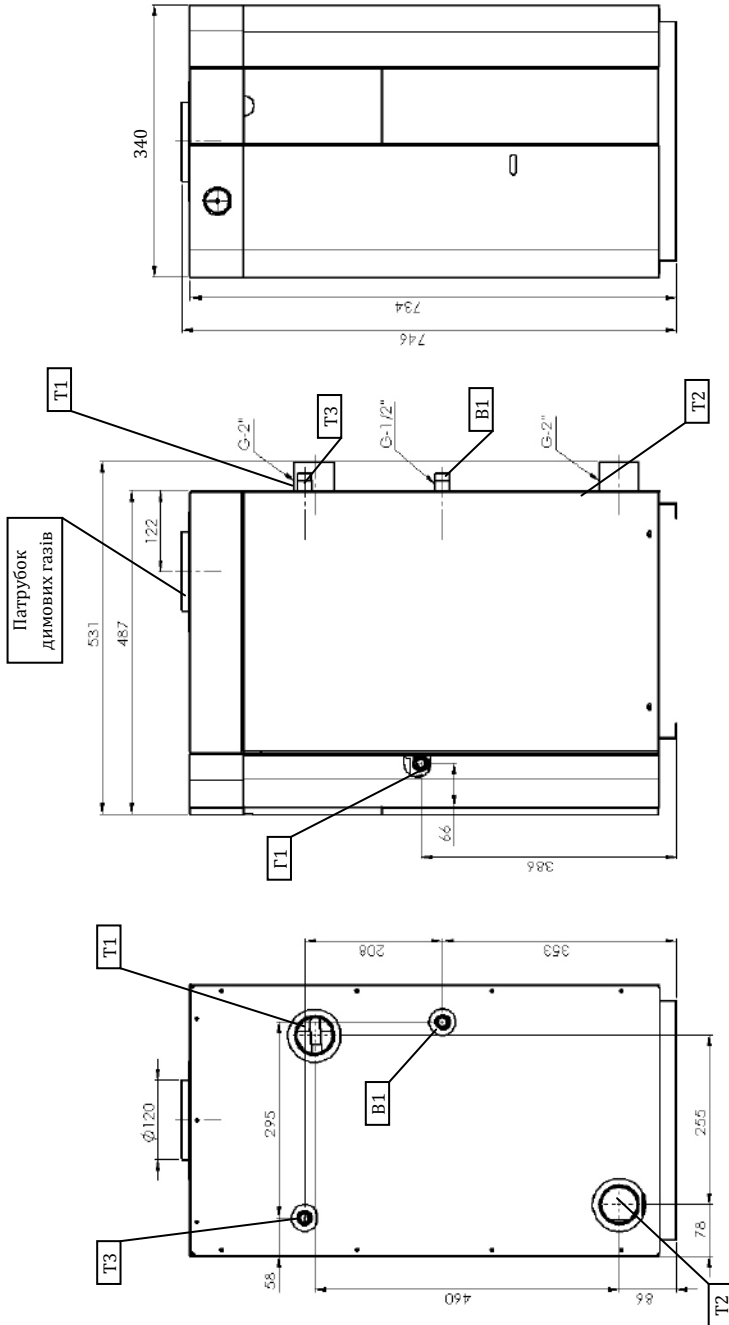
Установчі креслення апаратів КТ 8 ТS(П2) Б; «ЛЮКС»
